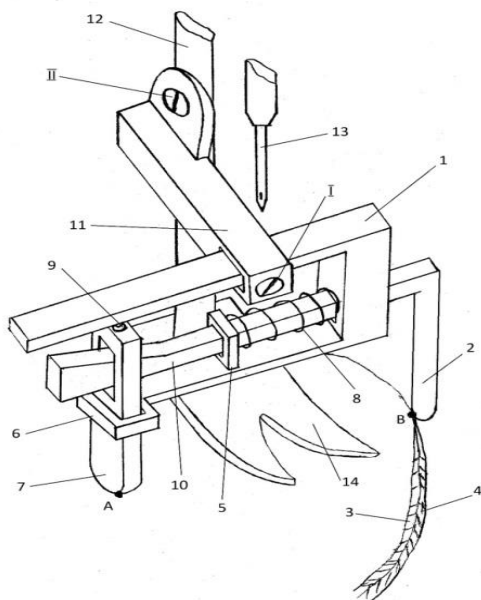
Транспортно-ориентирующее устройство с механической следящей системой для универсальных швейных машин: 1 – рамка; 2 – упор; 3, 4 – сшиваемые детали; 5 – стопорное кольцо; 6 – отверстие; 7 – прижим; 8 – пружина; 9 – винт; 10 – ползун; 11 – кронштейн; 12 – стержень; 13 – игла
